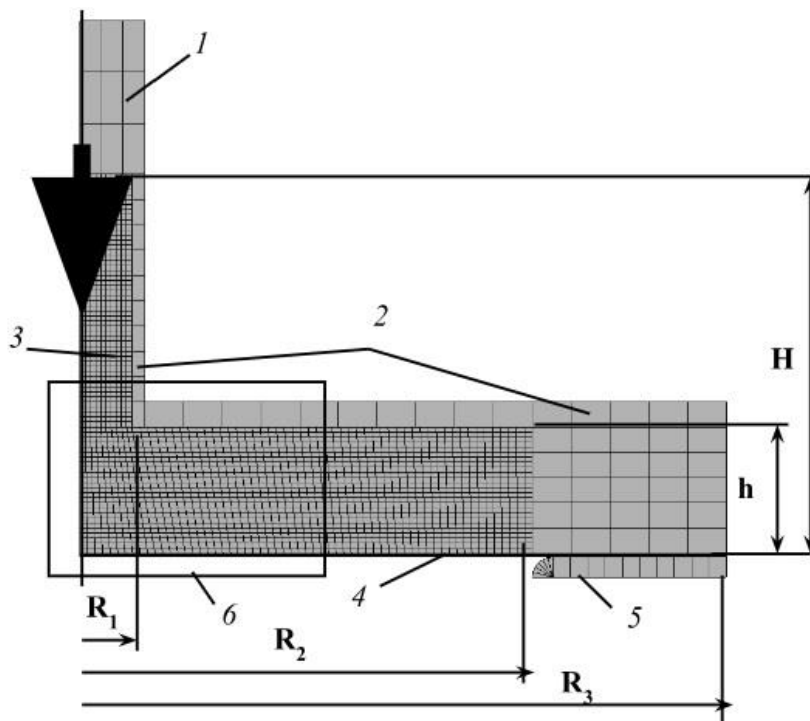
Схема розрахункової моделі (1 – жорсткий поршень, що імітує межу парогазової порожнини з високим тиском; 2 – камера; 3 – рідина; 4 – заготовка; 5 – витягувальне кільце):
